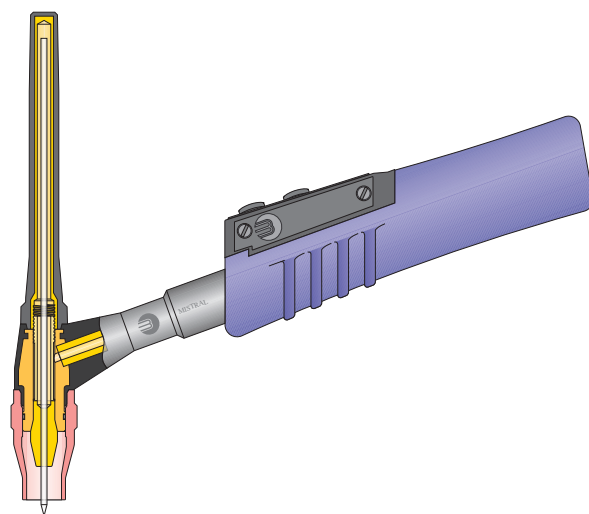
Gasgekühlter WIG-Schweißbrenner
